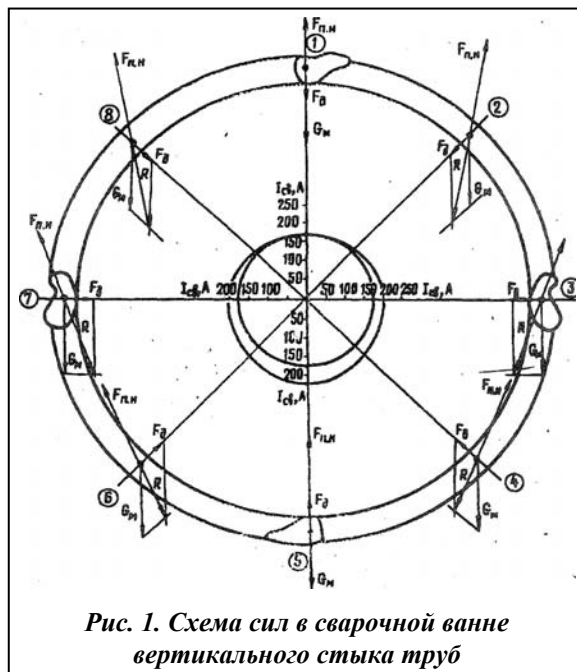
Схема сил в сварочной ванне вертикального стыка труб
